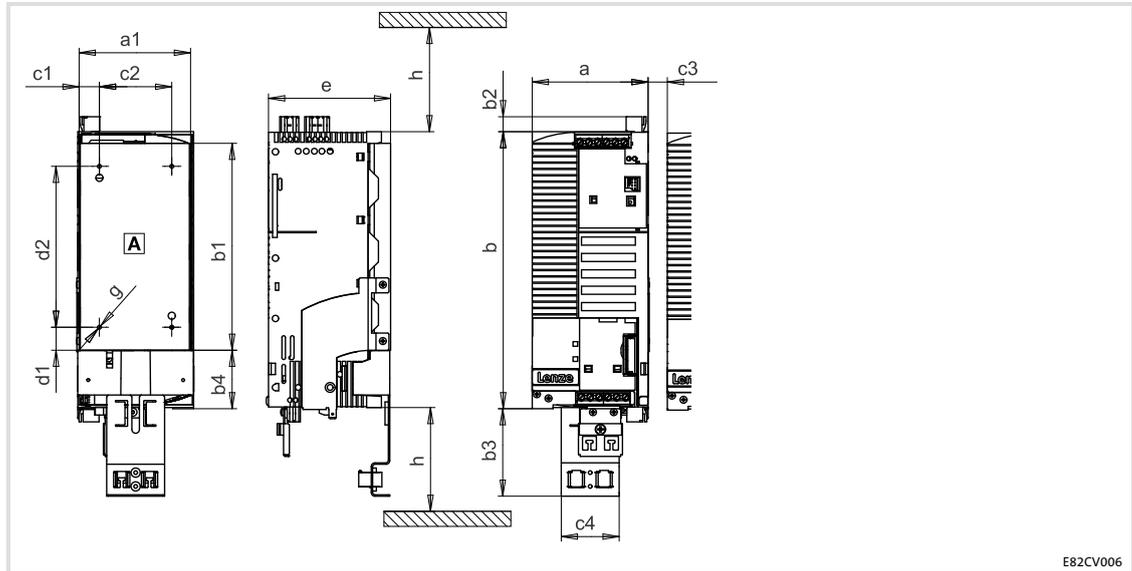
Abmessungen Montage in "Cold Plate"-Technik 3 ... 11 kW
